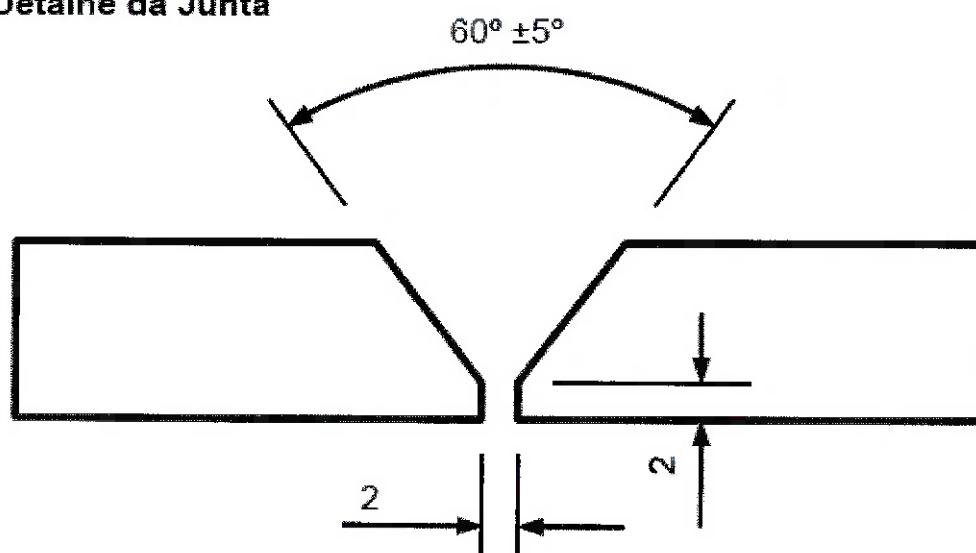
Detalhe da junta soldada (valores em mm)
